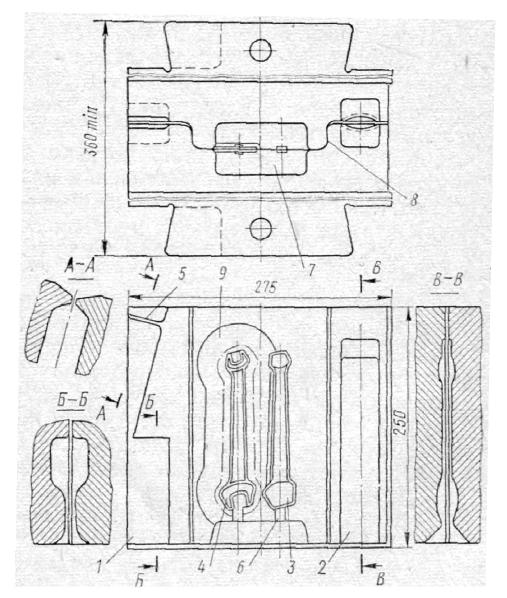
Схема гравюры многоручьевого молотового штампа: заготовительные ручьи: 1 — протяжной; 2 — подкатной; формующие ручьи: 3 — черновой; 4 — чистовой; другие элементы гравюры: 5 — отрубной нож; 6 — литниковая канавка; 7 — выемка под клещевину; 8 — замок; 9 — облойная канавка
